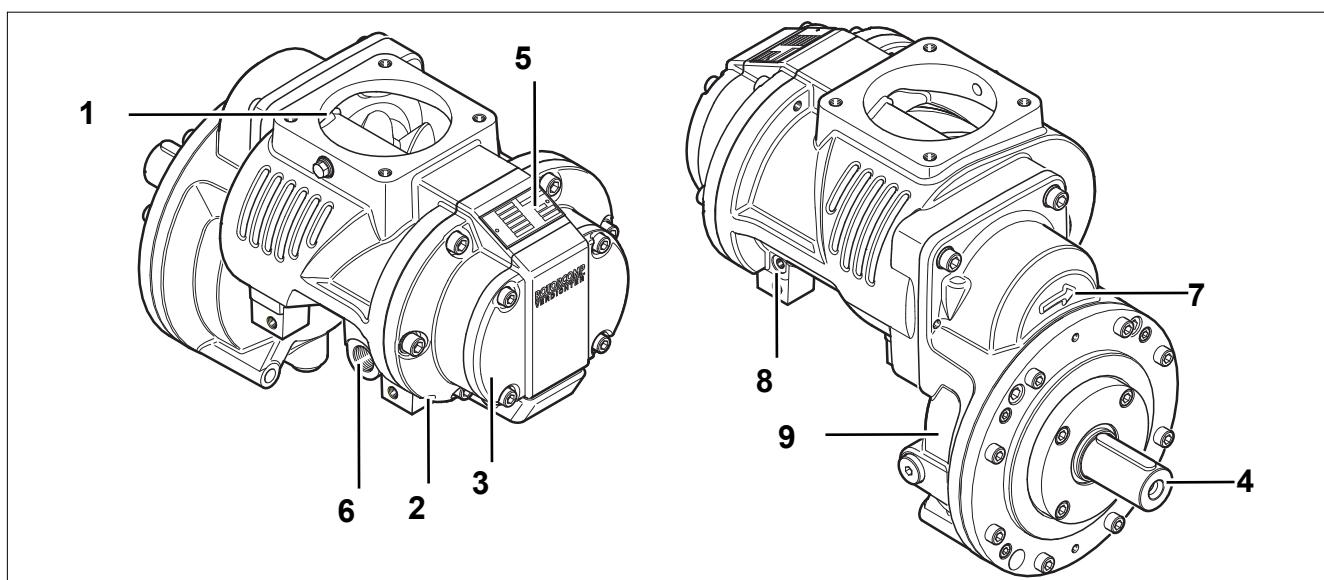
Винтовой блок EVO 9 GV (вертикальный редуктор)
